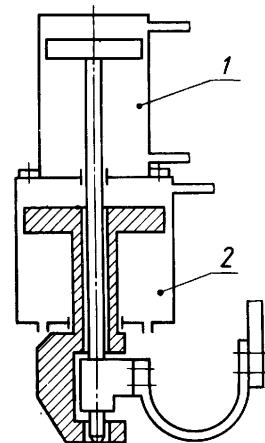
Универсальный ступень для сборки и сварки секций крыш
